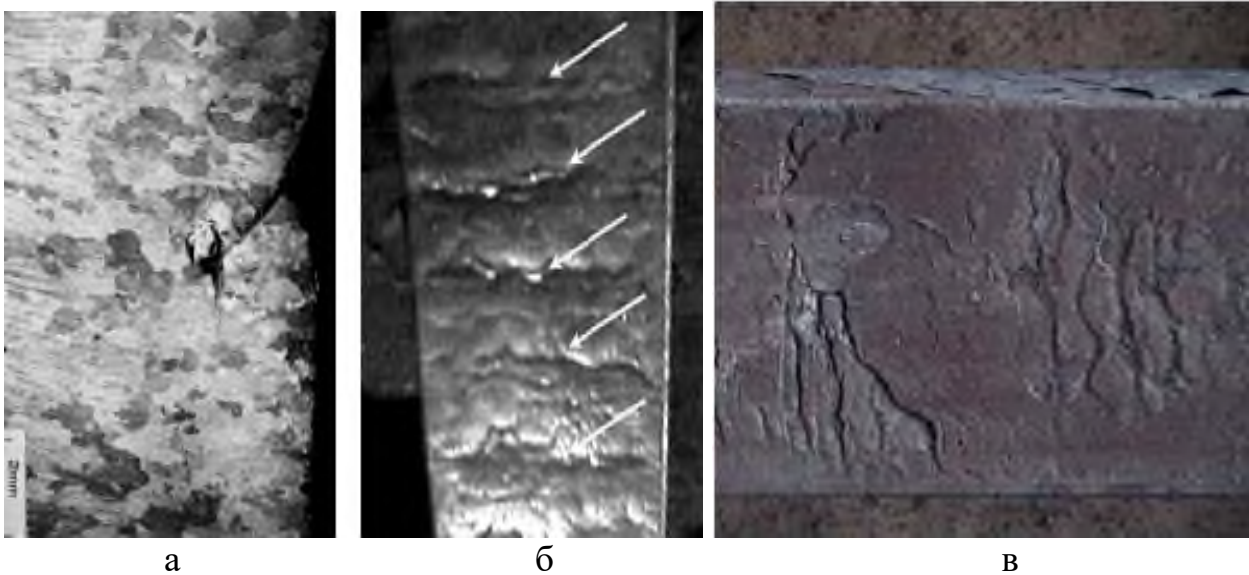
Поздовжній перетин зразка заготовки в місці розташування залівин (а) і її фото на поверхні заготовок (б, в)
